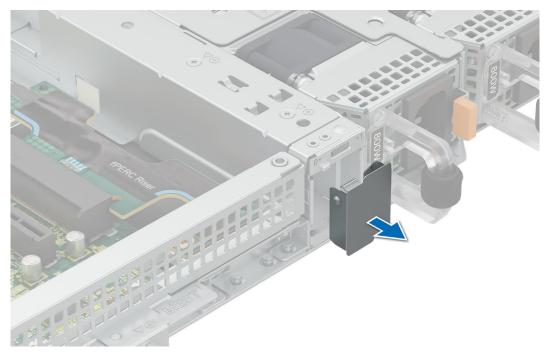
Entfernen des BOSS-N1-Platzhalters
